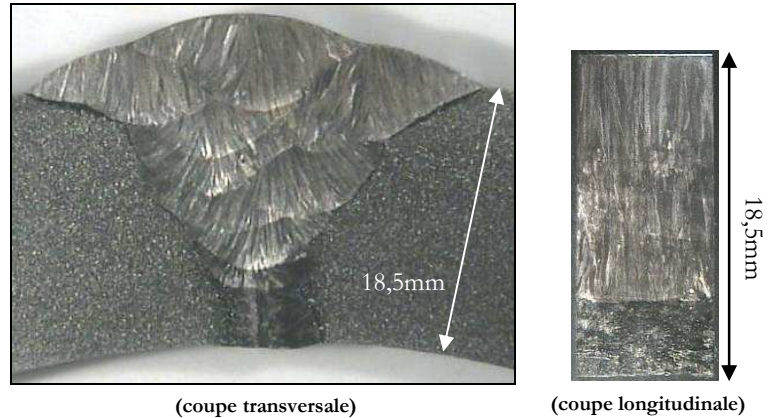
macrographies de soudures longitudinales de maquettes soudées
